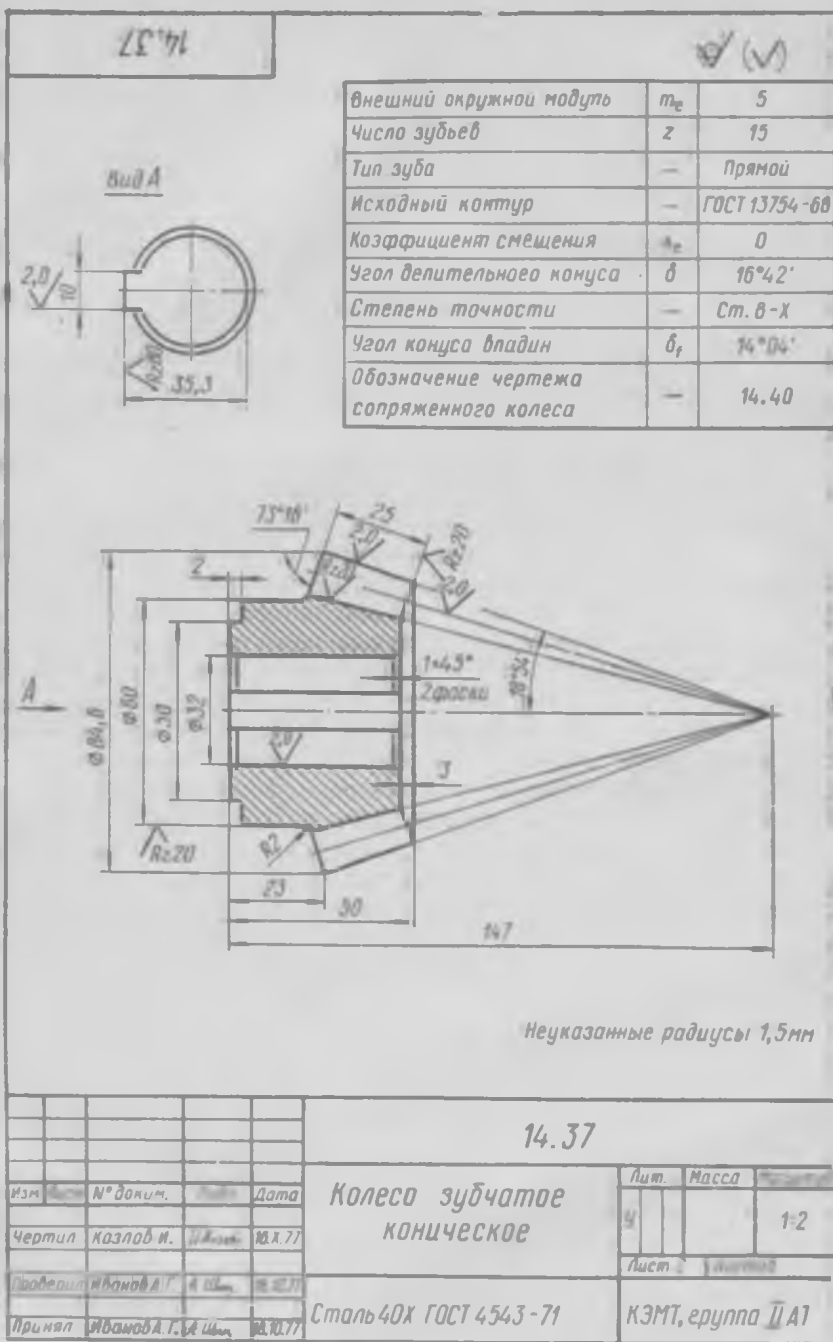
Рабочий чертёж конического зубчатого колеса (учебный)
